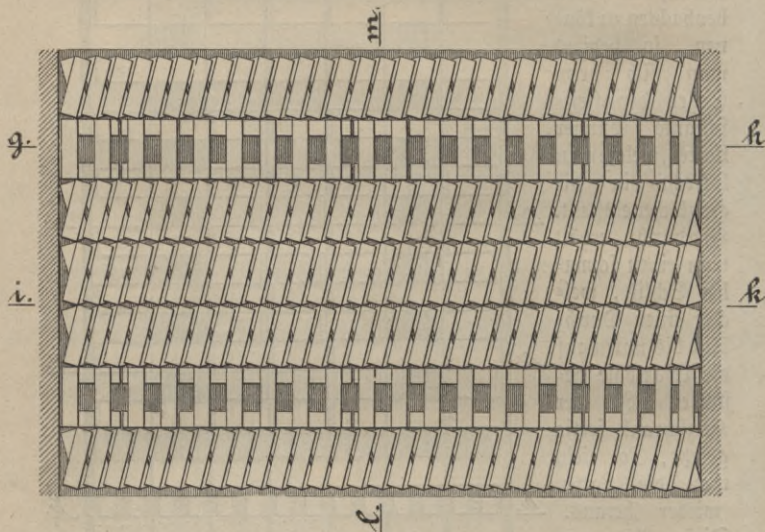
Einsatz. Grundriß. Schnitt a-b.
